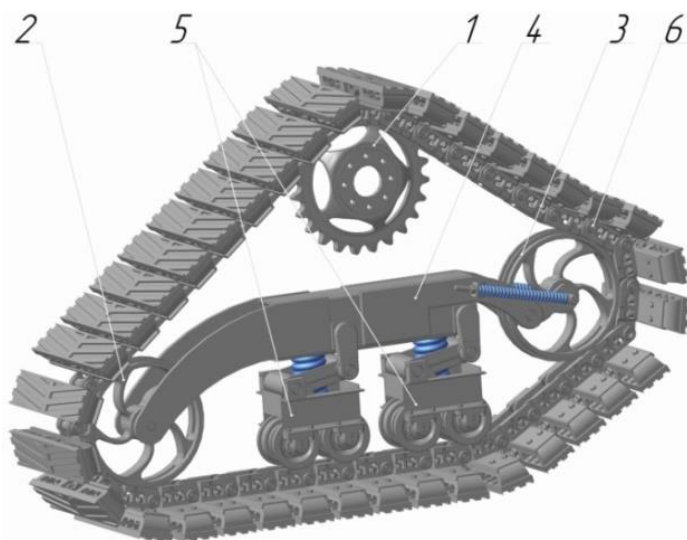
Сменный гусеничный движитель треугольной формы с резинокордными траками: 1 – ведущая звездочка, 2 – направляющее колесо, 3 – натяжное колесо, 4 – рама, 5 – опорные каретки, 6 – гусеничная цепь
